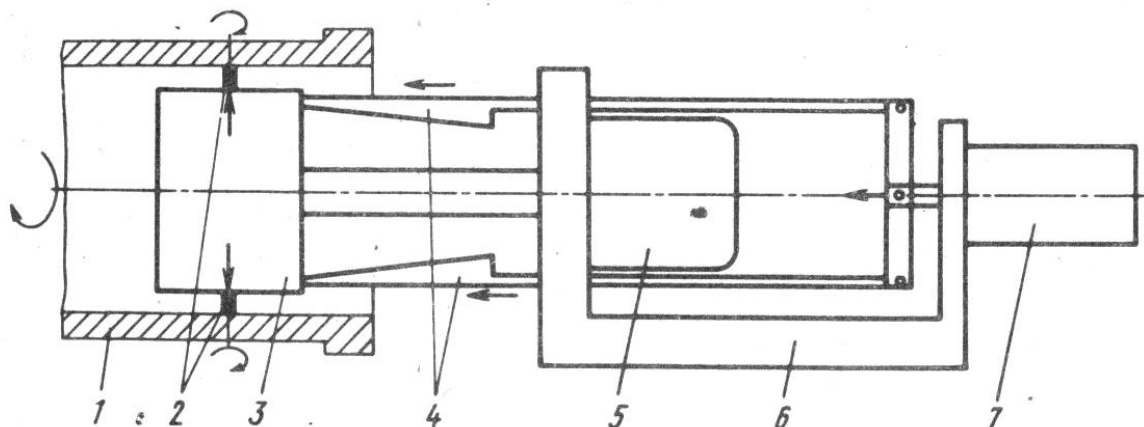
Принципова схема установки для фрикційного латунювання циліндрів двигуна обертовим штифтом.
